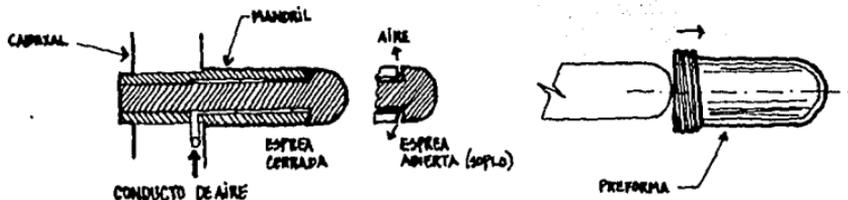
Corazón o Mandril de el molde de inyección de una máquina de Inyección-soplo.
